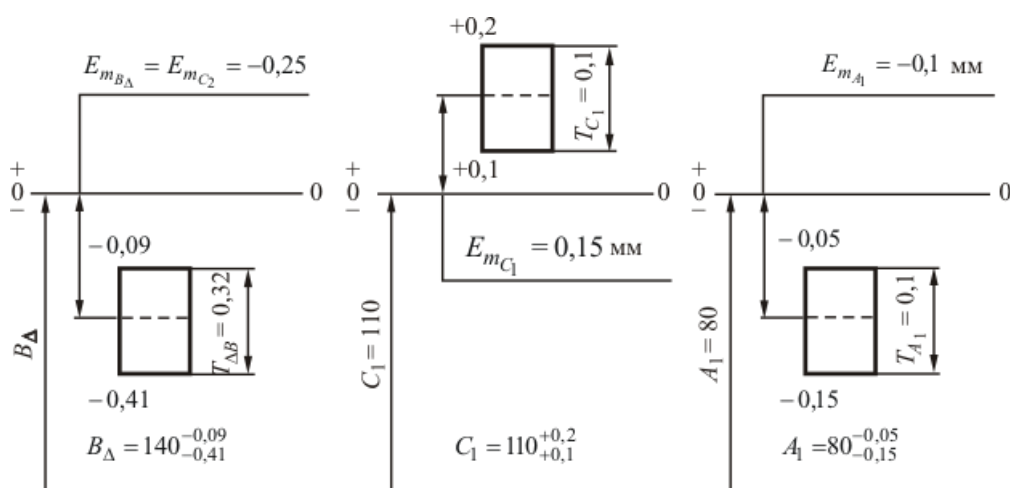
Схемы расположения полей допусков на операционные размеры
